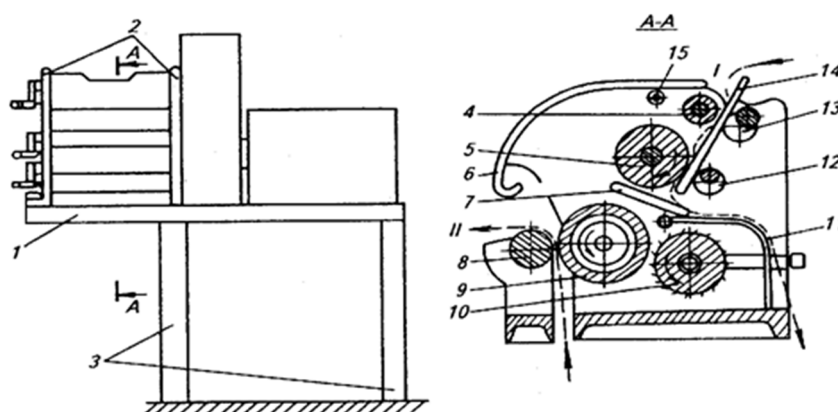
Машина універсальна ФОК для обробки кишок:
